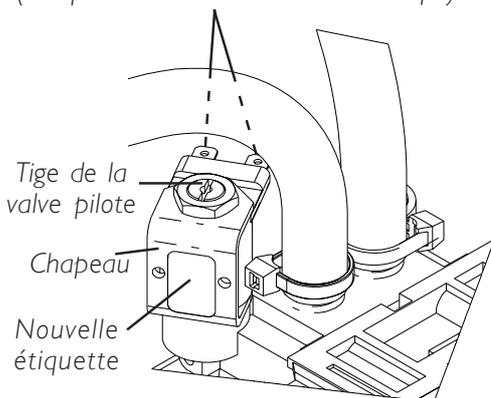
DEMONTAGE/INSTALLATION DES POUTRES ET JOINTS TORIQUES DE LA VALVE PILOTE
